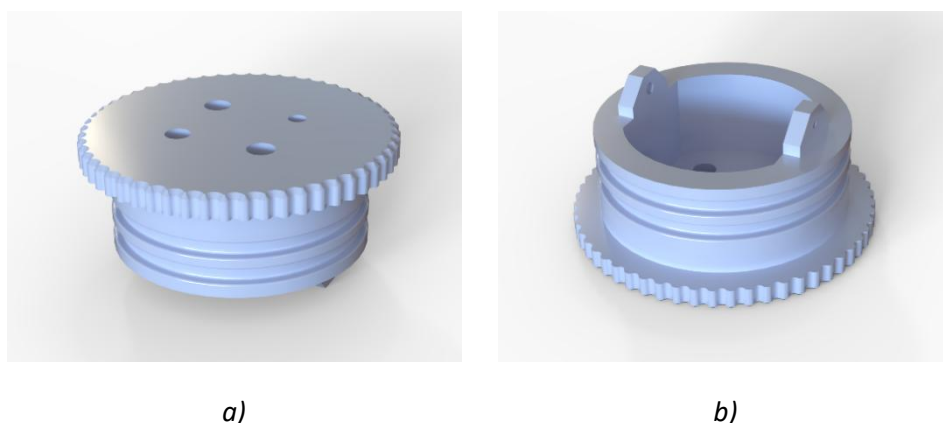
PCB Cradle. a) Forside av PCB Cradle med spor for encoderkort og step-down-modul, b) Bakside av PCB Cradle med spor for Sensor Shield
